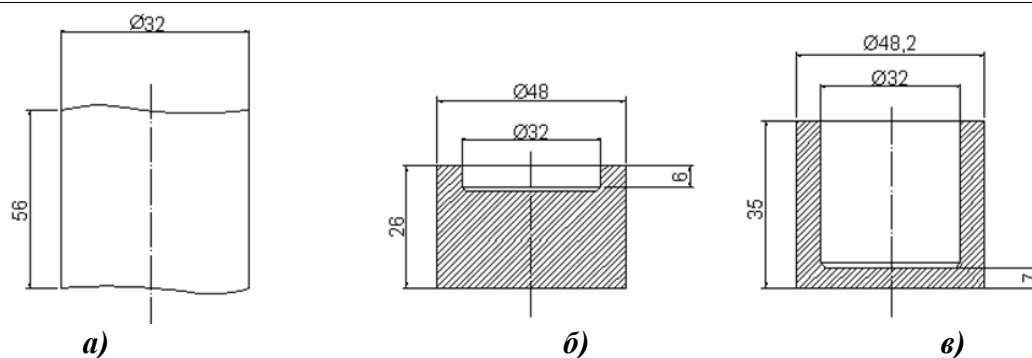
Новый технологический процесс детали «поршень тормозного цилиндра»: а – заготовка/70 тонн; б – 1-ый переход/калибровка/120 тонн; в – 2-ой переход/обратное выдавливание/160 тонн)
